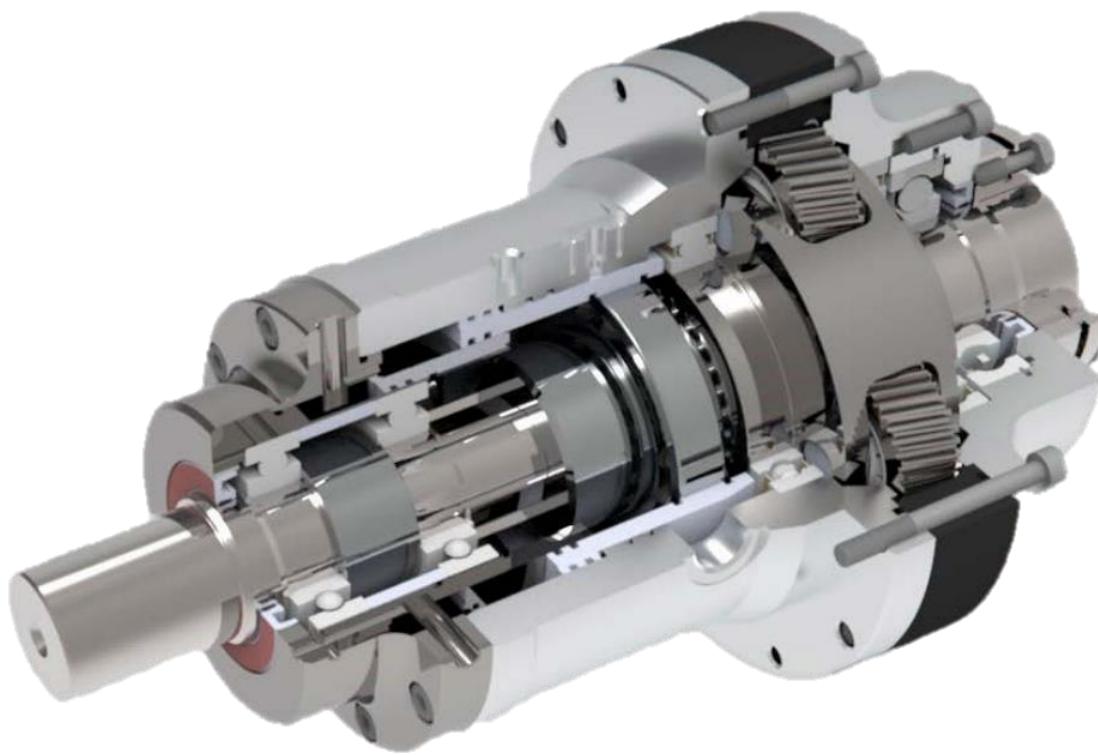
Двухступенчатая КПП 2PG-CRT Gearbox от компании Compact Reducer Technology
